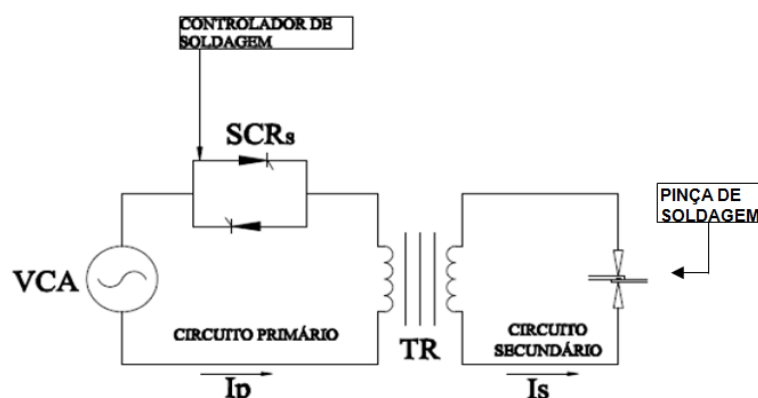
Representação dos principais componentes de um equipamento de soldagem por resistência elétrica (Pinheiro, 2010).
